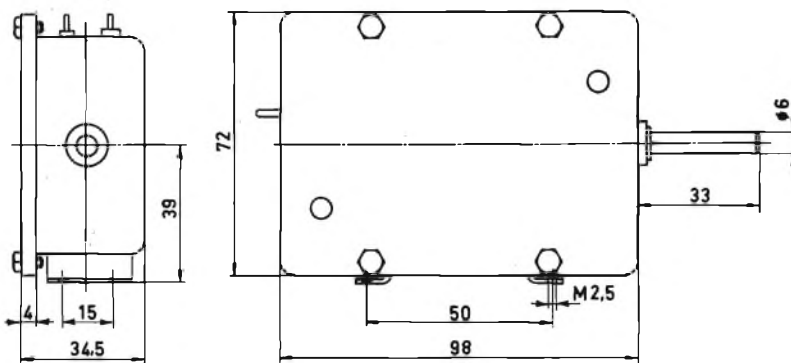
Dimensioni di ingombro del sintonizzatore UHF tipo MG/0170-00, e delle varianti tipo 180 e 190.
